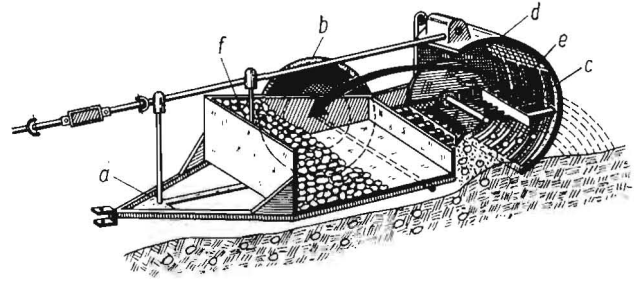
Steinsammler mit Rotorkämmen; a Profiltrahmen; b Laufräder, c Rechen, d Rotationstrommel, e Sammelkammer, f Bunker
